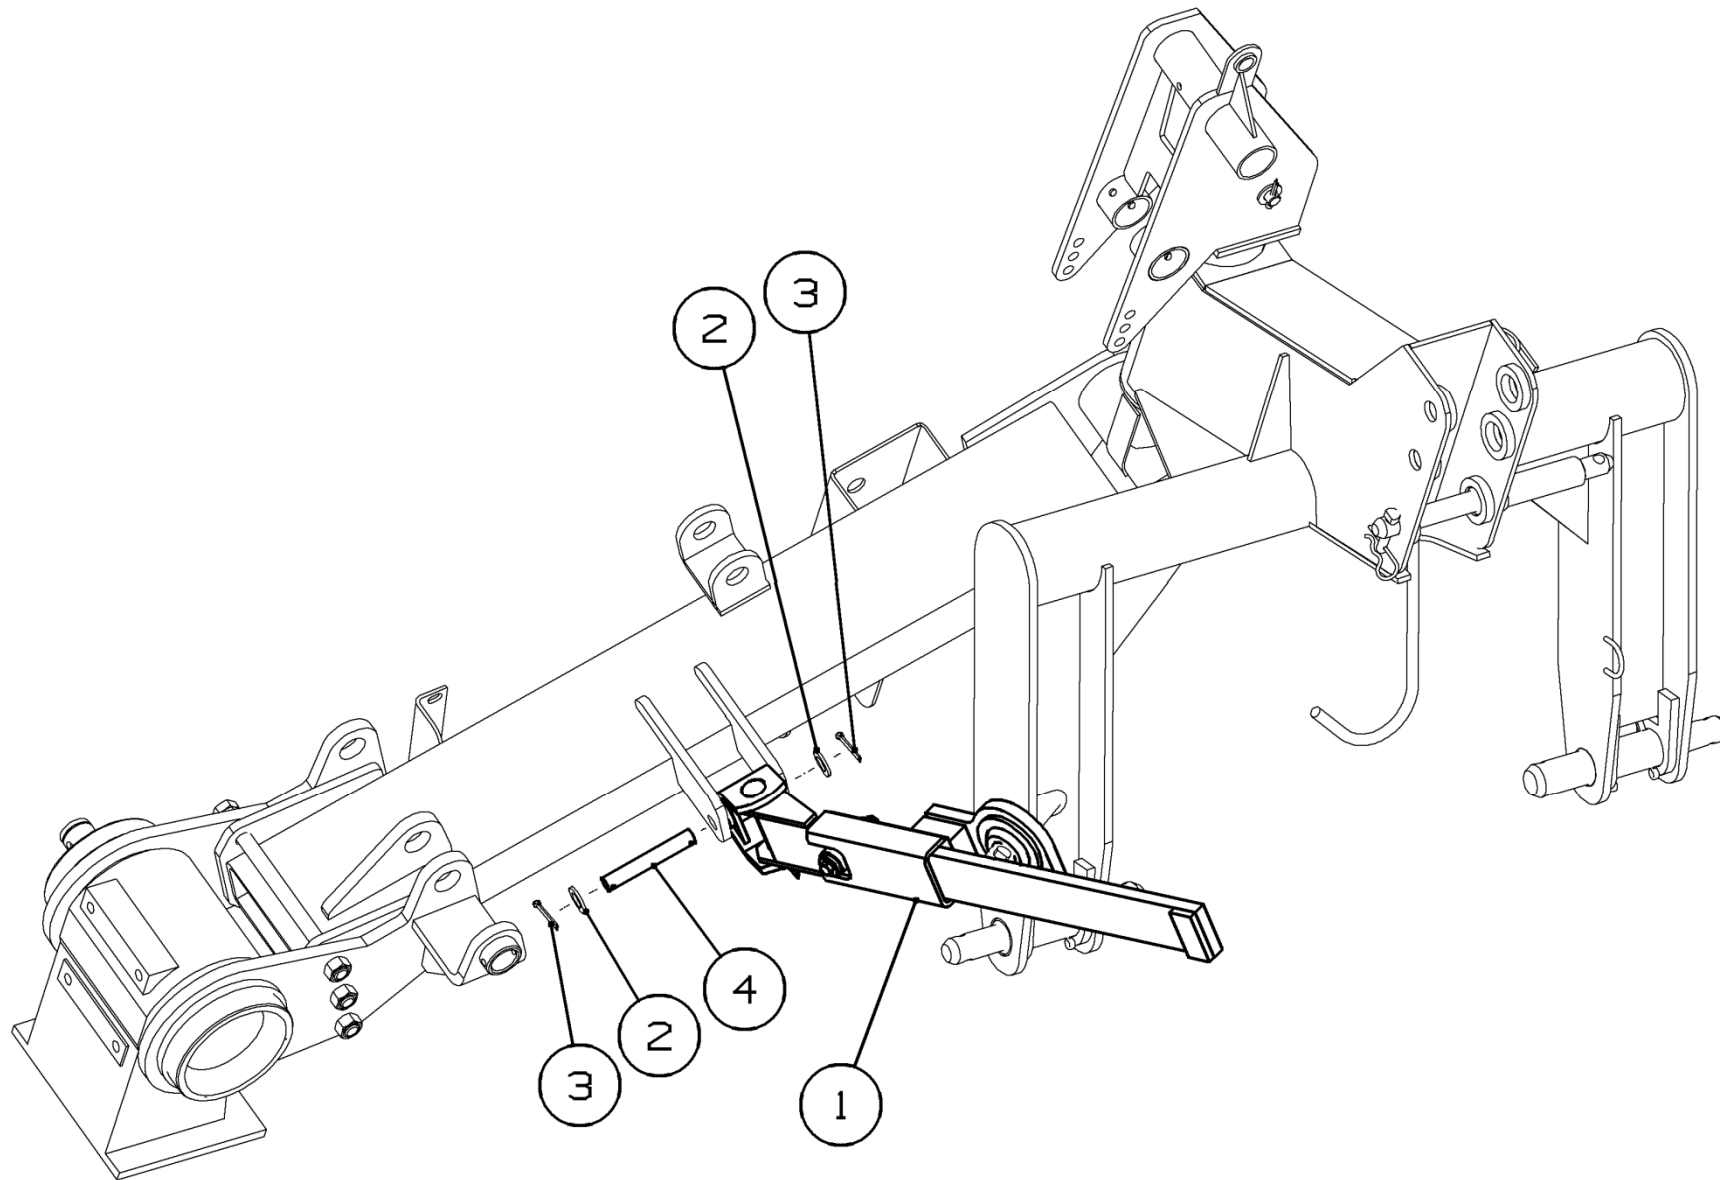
КРК-2.4.06.000 Установка предохранителя
